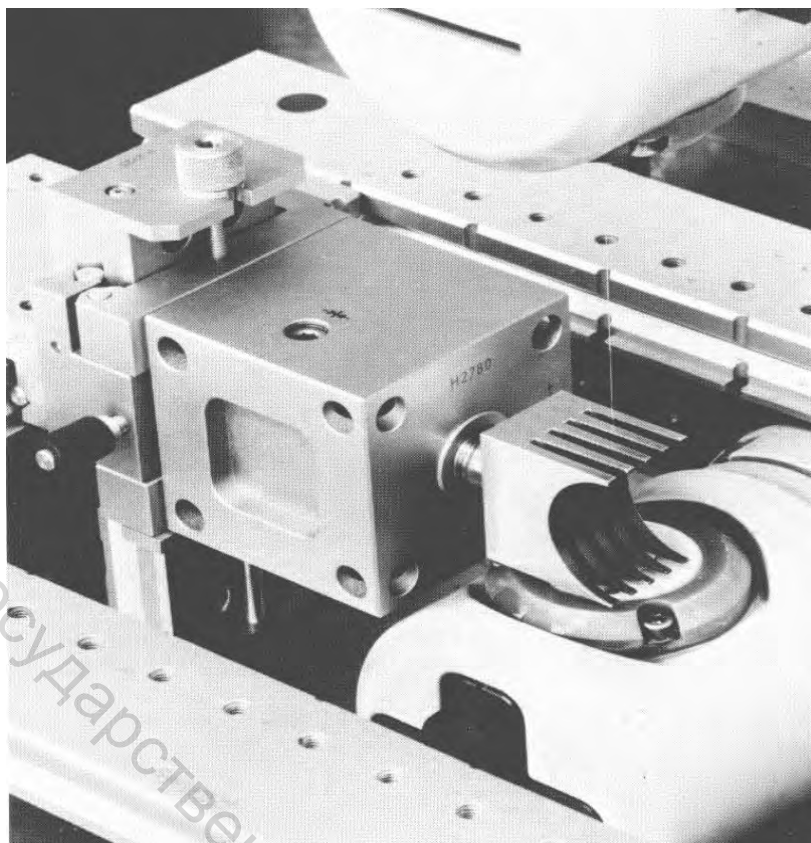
Фотография поворотного приспособления, используемого для вырезания
